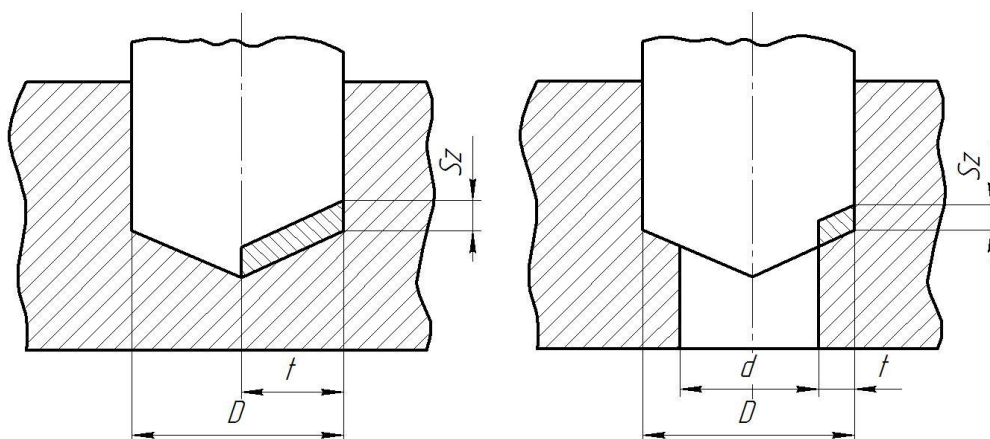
Схема різання при свердлінні й розсвердлюванні
